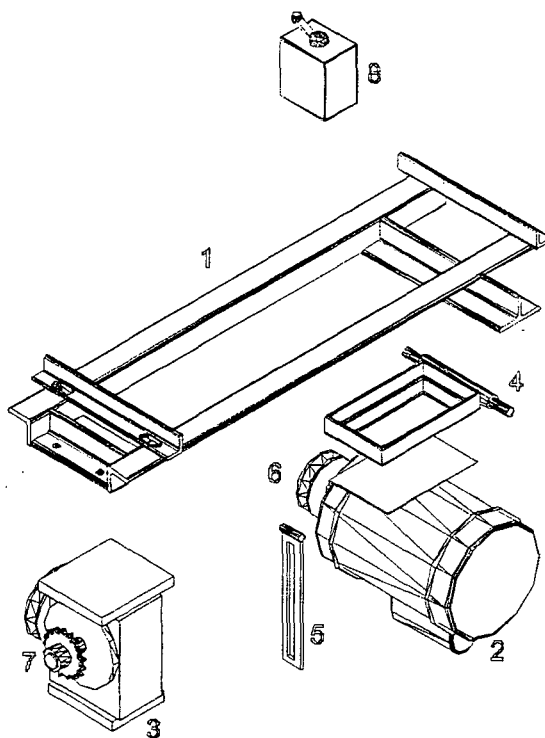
Desenho das partes do sistema de transmissão: 1 – suporte do motor e redutor; 2 – motor elétrico; 3 – redutor; 4 – suporte do motor; 5 – esticador da correia; 6 – polia do motor; 7 – engrenagem do redutor; 8 – interruptor.
